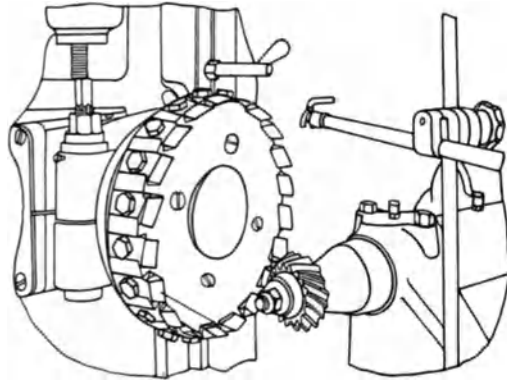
Gleason Spiralzahnkegelradfräsmaschine.
